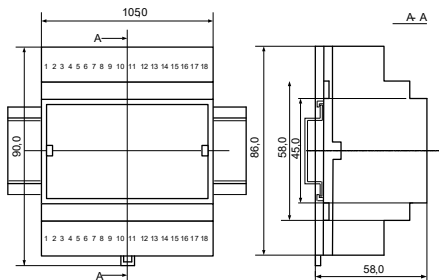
Габаритные и присоединительные размеры модуля
